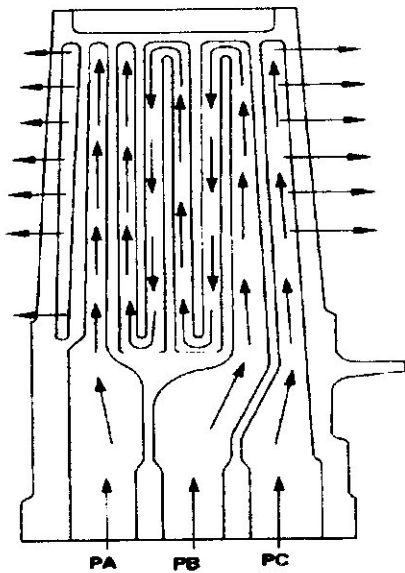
Coupe longitudinale d'aubage du Fig. I.16.
